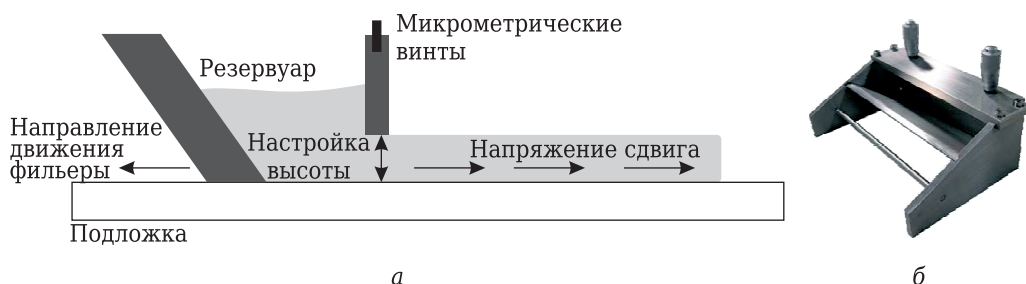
Схема процесса отливки пленки на ленту (а); фильера с двумя микрометрическими винтами (б), которые контролируют зазор между скребком (doctor blade) и подложкой [222]
